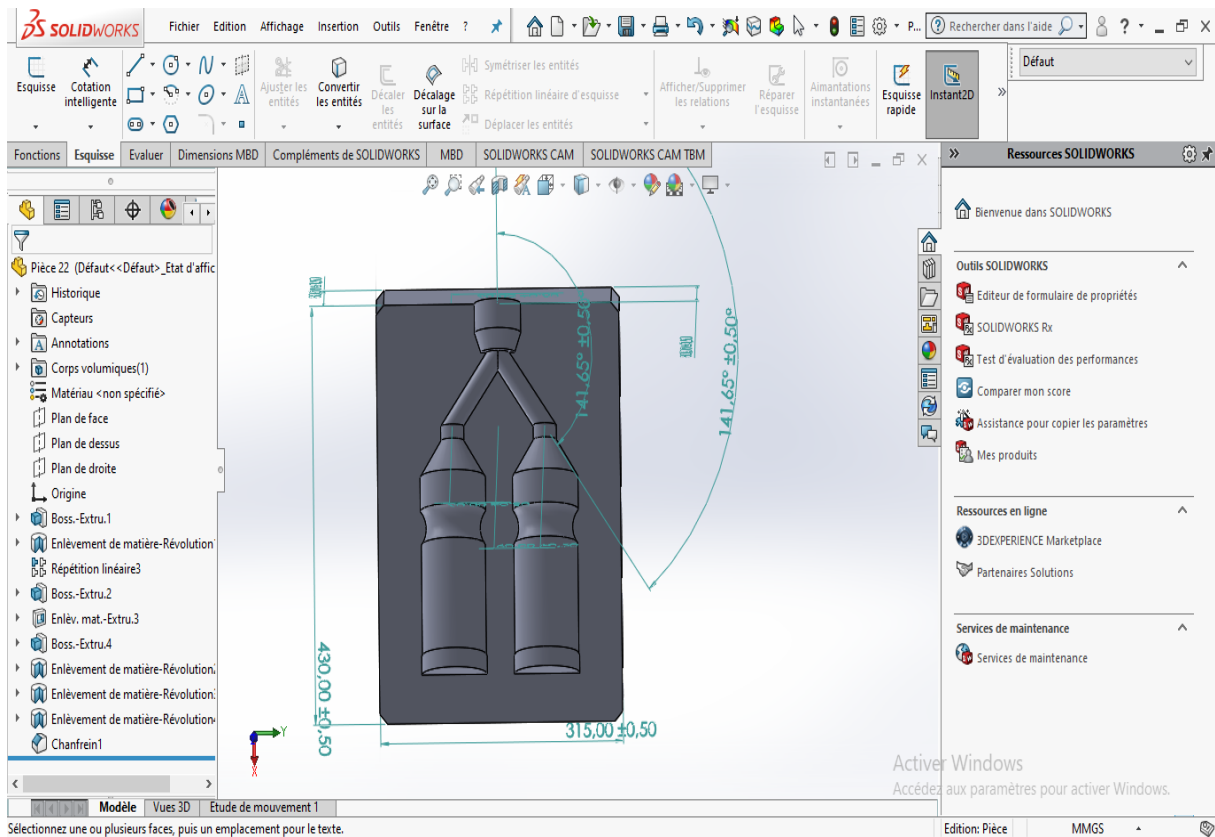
Les dimensions du moule d'injection par soufflage sous SOLIDWORKS
